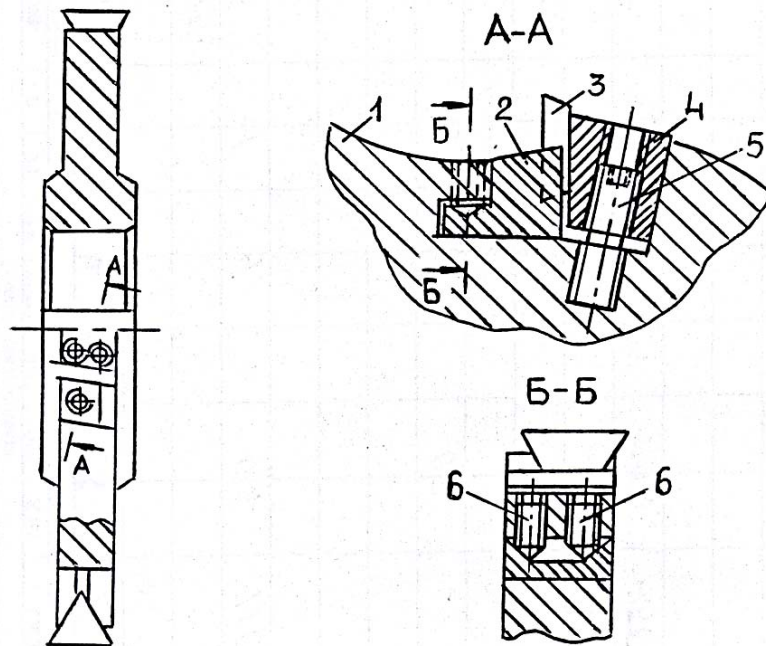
Конструкция сборной дисковой трехсторонней фрезы M90
